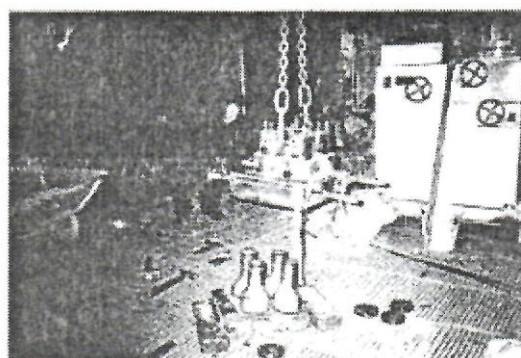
Литые заготовки корпусов коронок после извлечения из четырехместного кокиля
